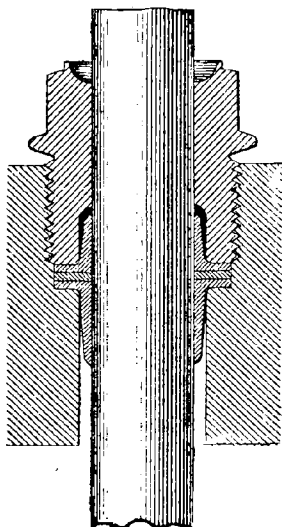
Garniture pour piston de machine hydraulique (coupe).
